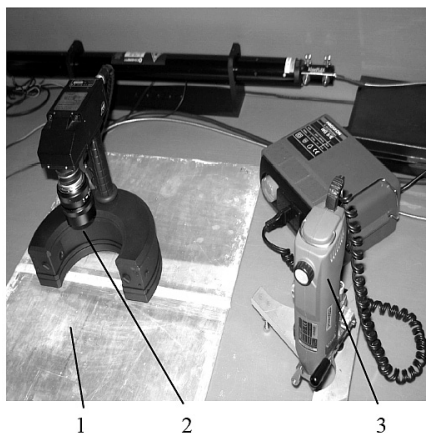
Образец со сварным швом (1), оптический модуль (2), инструмент для сверления отверстий (3).
